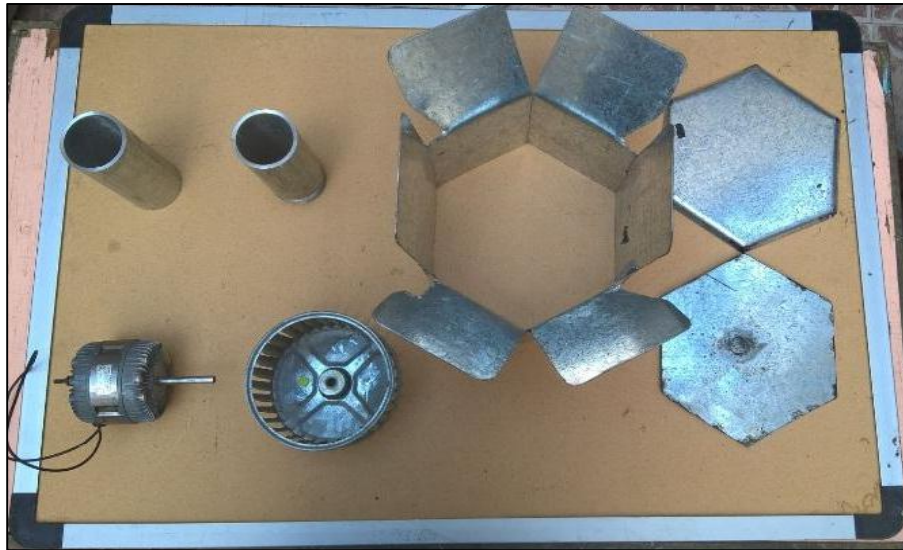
Cilindros, motor, molde y placas para tapa del molde
